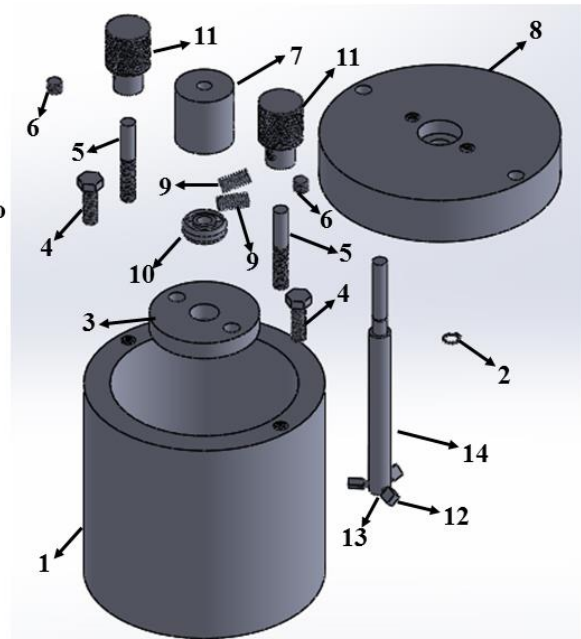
Vista explosionada de todas las piezas que conforman el mezclador de paletas inclinadas.
